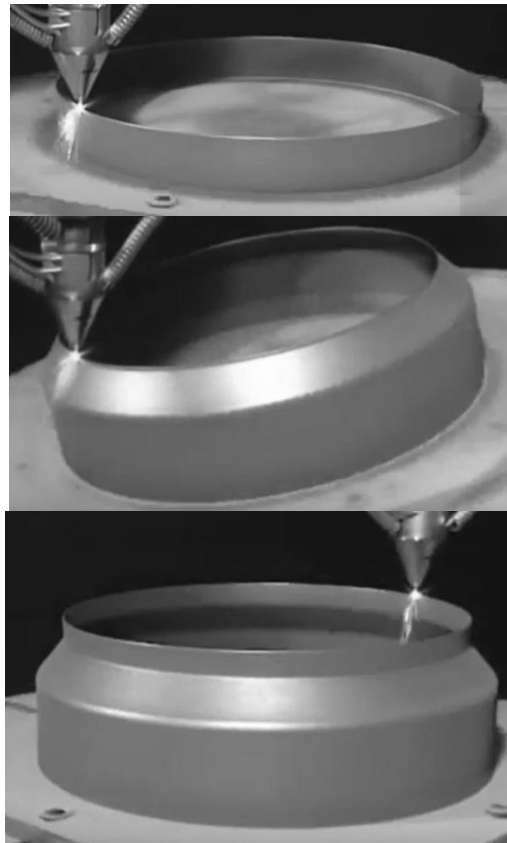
Последовательные стадии изготовления металлической детали по SLM-технологии
